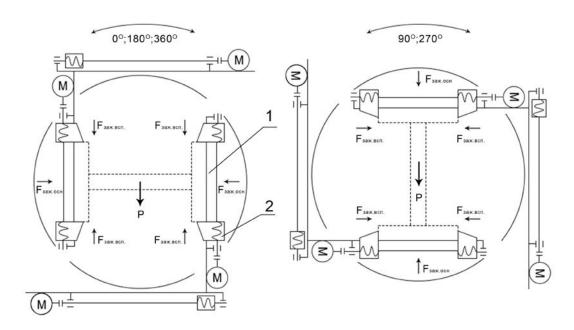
Схема зажатия заготовки поворотным порталом-кантователем: 1 – губка основного механизма захвата; 2 – губка вспомогательного механизма захвата
